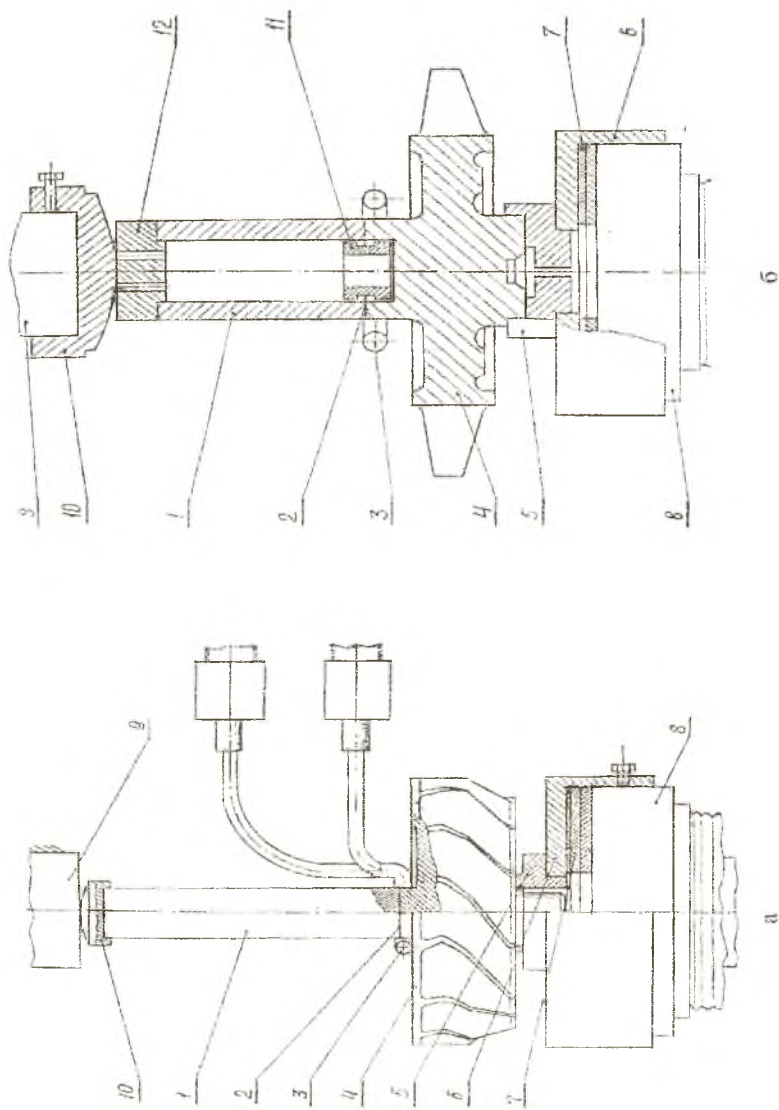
Оснастка для диффузионной сварки рабочих колес роторов турбин с валами сплошного сечения (а) и полого исполнения (б)
